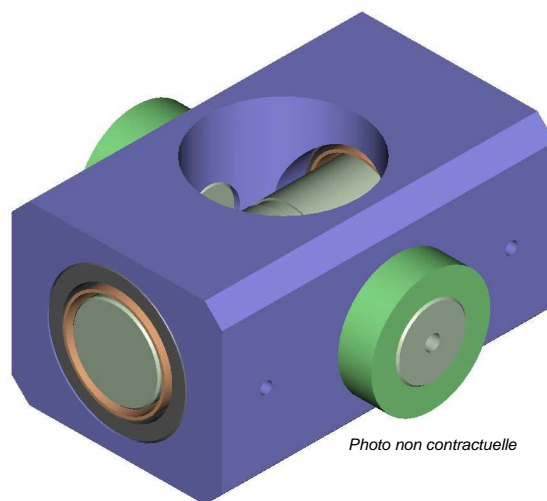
PLATEAU PLANIMETRIQUE ROTULE DE PRECISION PPR 2-2-2-7000-1-0-0
